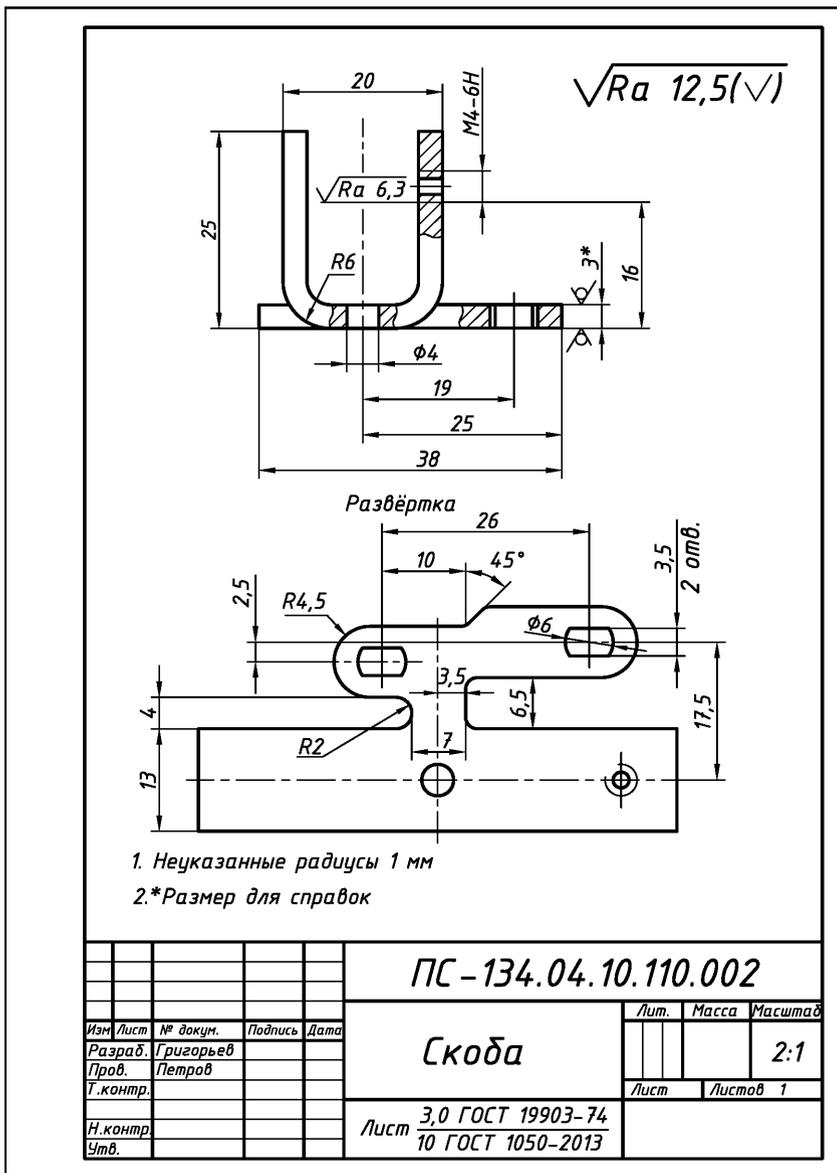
Оформление рабочего чертежа гнутой детали из тонколистового металла
